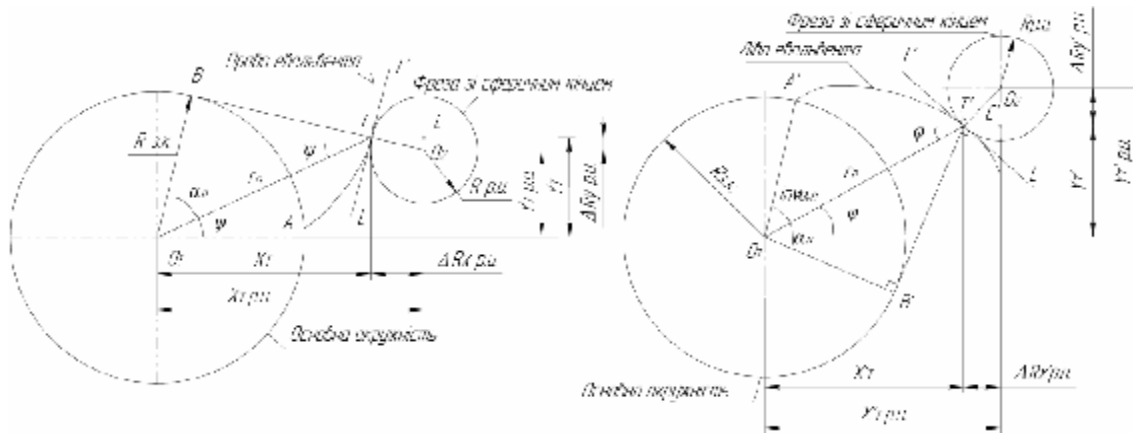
Розташування фрези на лівій та правій евольвентній поверхні у процесі обробки (вид з гори)
